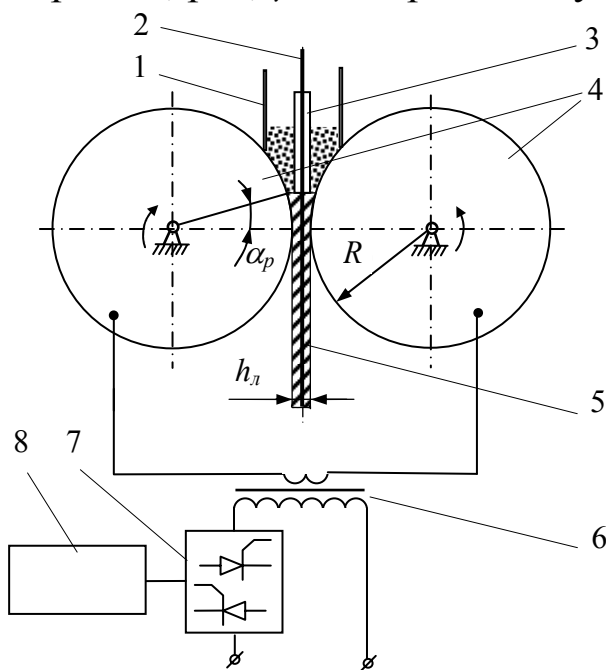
Схема электроконтактной прокатки спеченных лент: 1) бункер; 2) металлическая сетка; 3) разделительные пластины; 4) валки; 5) спеченная лента; 6) трансформатор; 7) контактор; 8) регулятор циклов сварки
